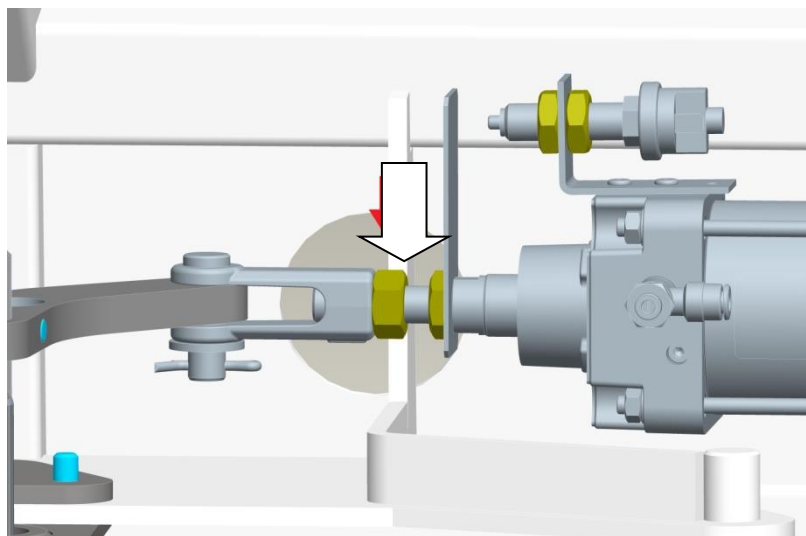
Місця підтягування кріплень вилок циліндрів
